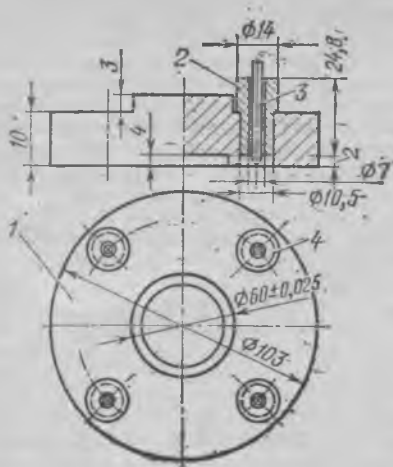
Кондуктор для разметки отверстий во фланцах привода и кардана силового вала вентилятора охлаждения генератора: 1 — кондуктор; 2 — направляющие втулки (4 шт.); 3 — кернер (форсуночная игла диаметром 100 мм); 4 — отверстия
